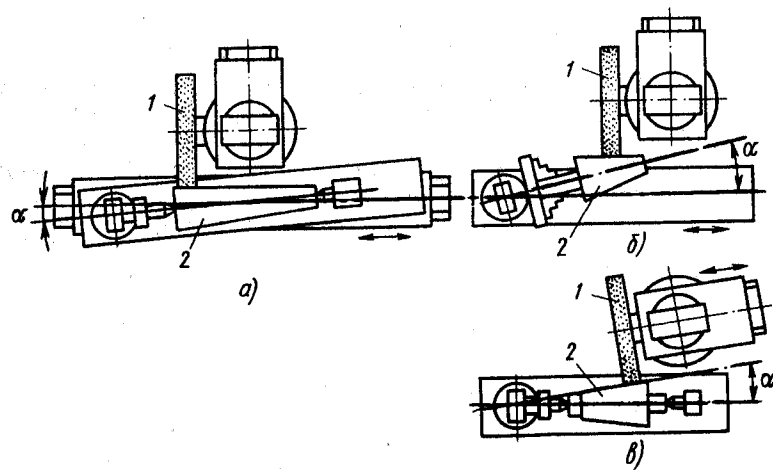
Шлифование конических поверхностей путем установочного поворота на половину угла при вершине конуса:
